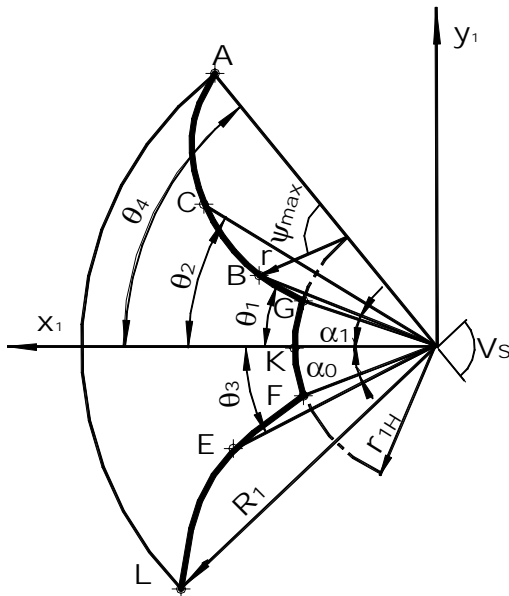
Профиль винтовой канавки ведущего винта компрессора
